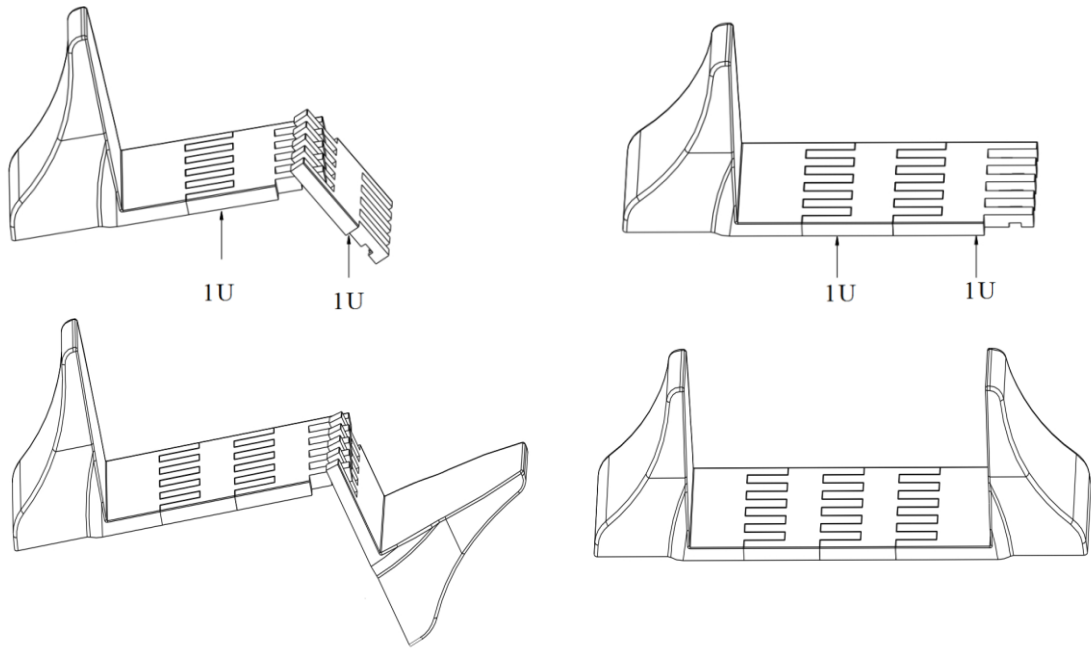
Пластиковая вставка для блока дополнительных батарей
